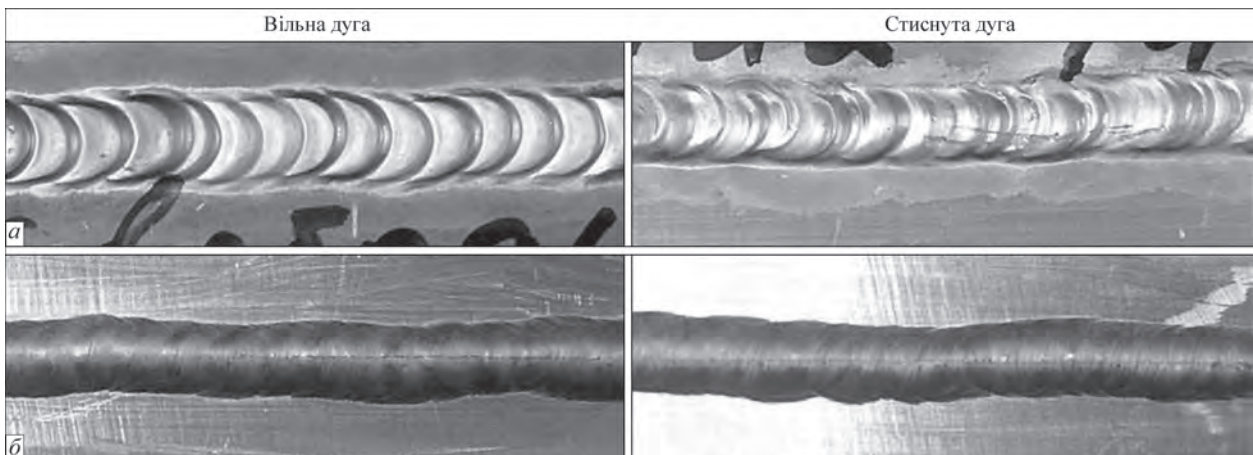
Зовнішній вигляд зварних з'єднань у стані після зварювання: а – лицьова поверхня шва; б – корінь шва
